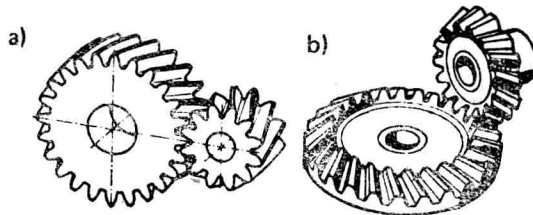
齿轮副 a. 圆柱齿轮副 b. 圆锥齿轮副
